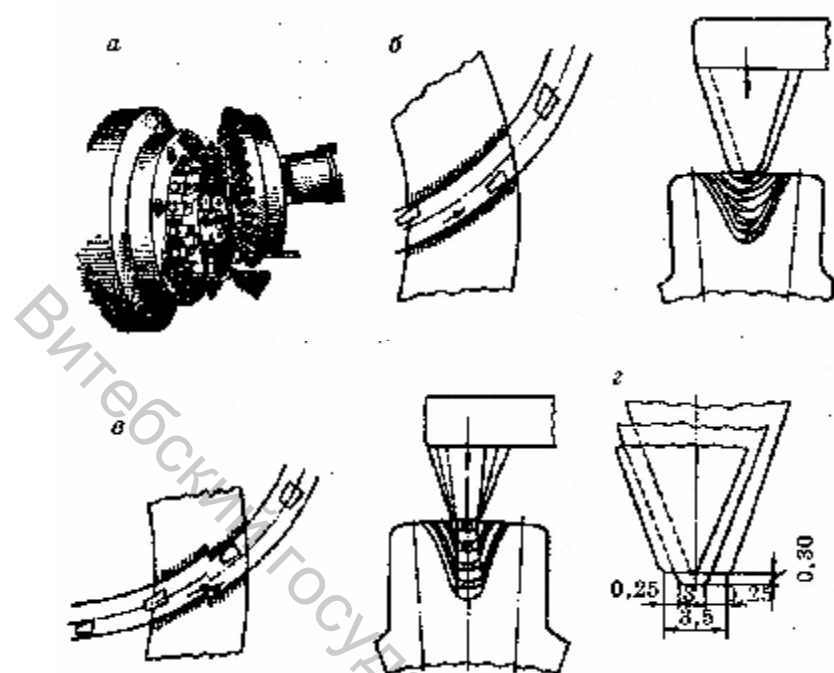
Нарезание конического зубчатого колеса с криволинейными зубьями: а — односторонняя резцовая головка; б — схема работы двусторонней 1 головки; в — схема работы трехсторонней головки
